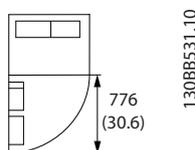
Пространство перед корпусом IP21/IP54, типоразмер F8
